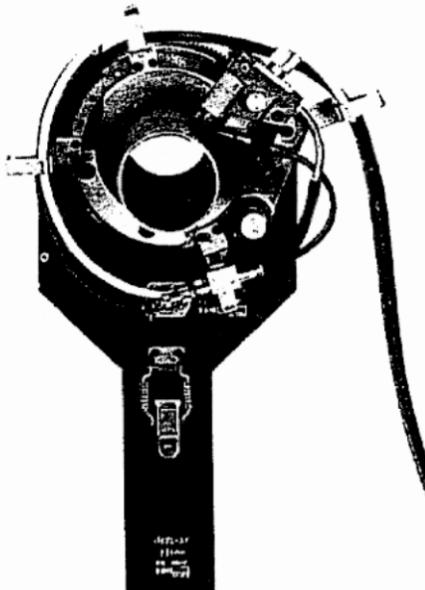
Сварочная головка для труб малого диаметра
